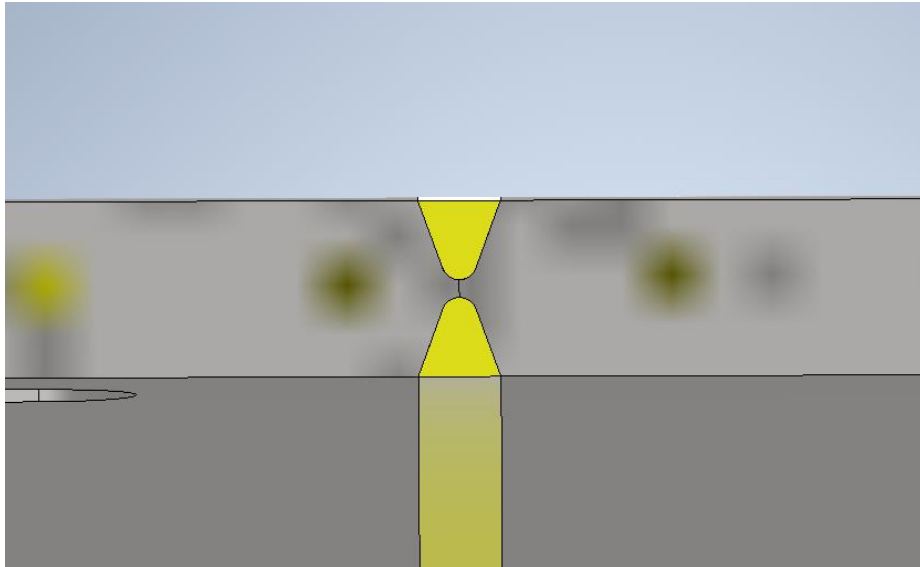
Modelo 3D de soldadura a tope [Elaboración propia]
